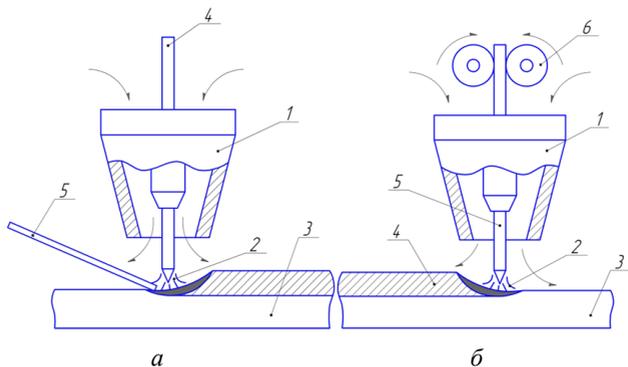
Схемы сварки в защитных газах неплавящимся (а) и плавящимся (б) электродами: 1 — горелка; 2 — электрическая дуга, 3 — основной металл; 4 — электрод; 5 — присадочная проволока; 6 — ролики
